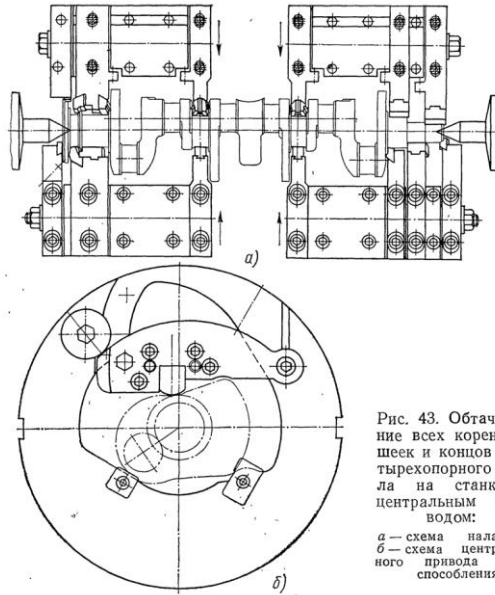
Обтачивание всех коренных шеек и концов четырехпорного вала на станке с центральным приводом:
